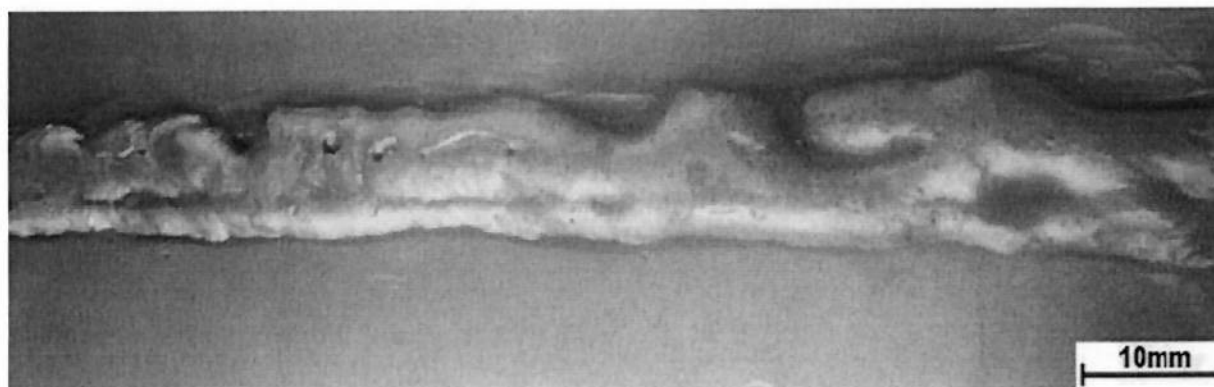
Aspecto visual da soldagem da junta soldada com 100% Argônio.
